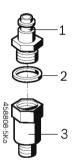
Сборка возвратного переходника с резьбовым соединением
